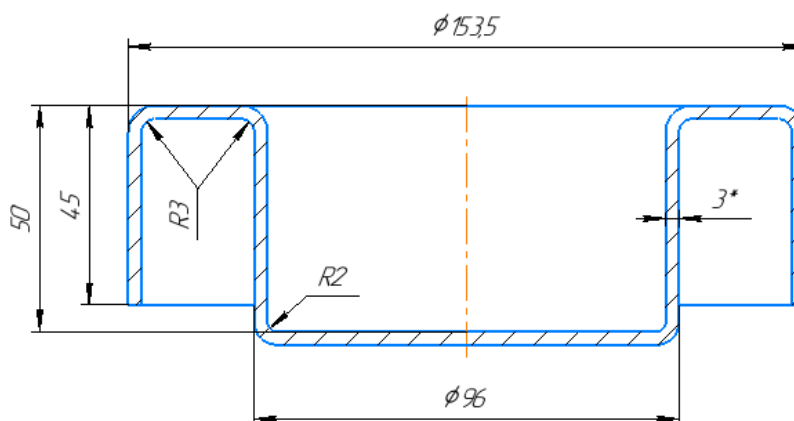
Эскиз заготовки после обратной вытяжки фланца
